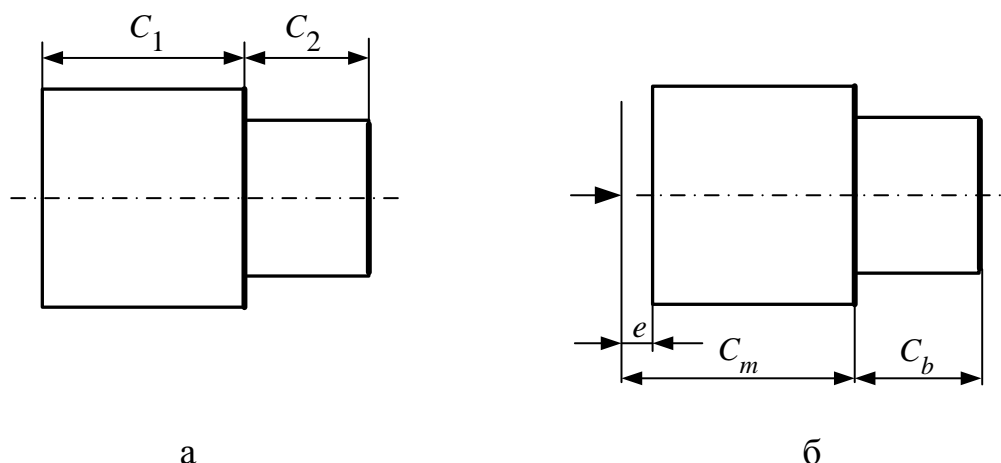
Эскиз детали (а) и схема (б), поясняющая место размеров C_m и C_b в формировании точности размера C_2 с помощью инструмента и двух упоров на станке
